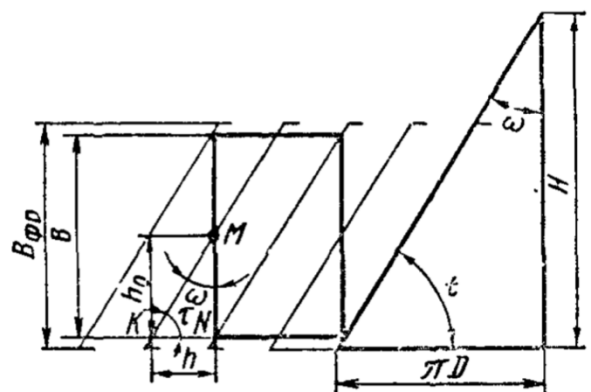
розгорнення поверхні різання при роботі циліндричною фрезою із гвинтовим зубом
